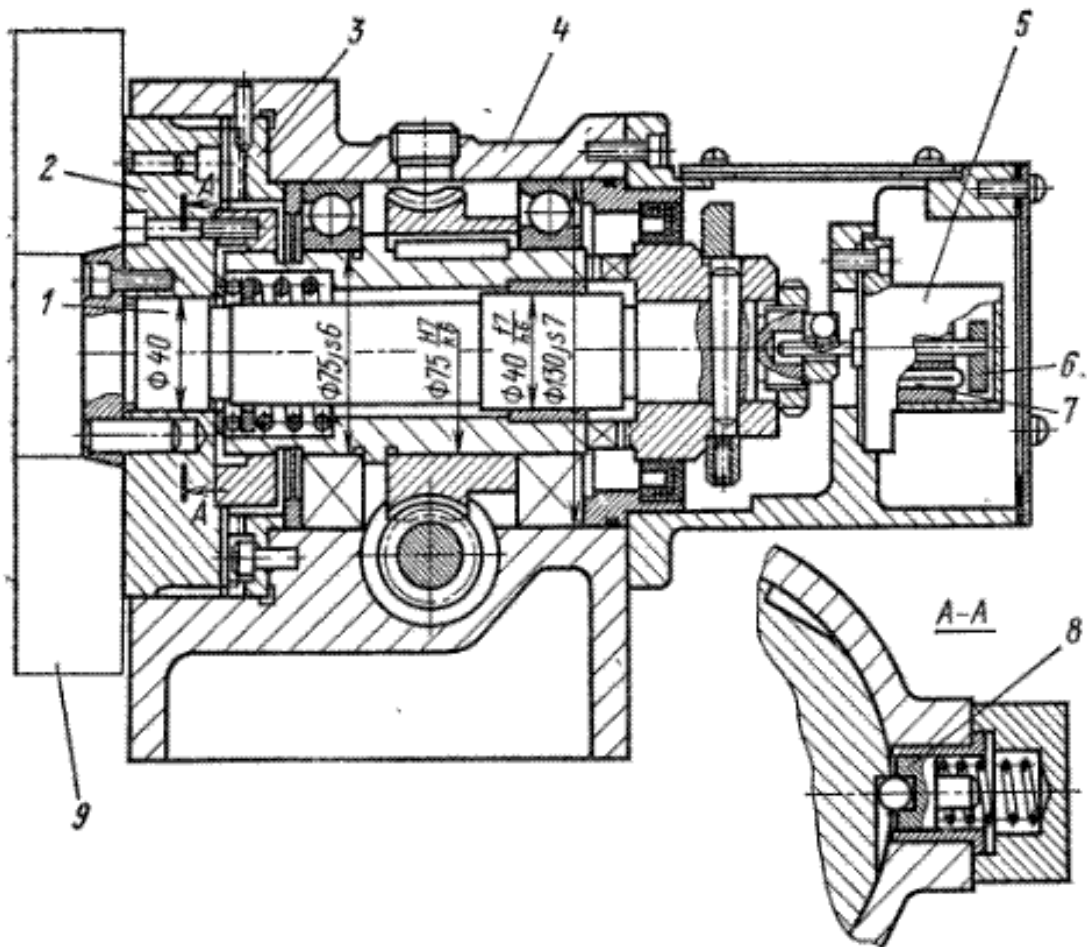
Револьверна головка верстата 16К20Ф3
